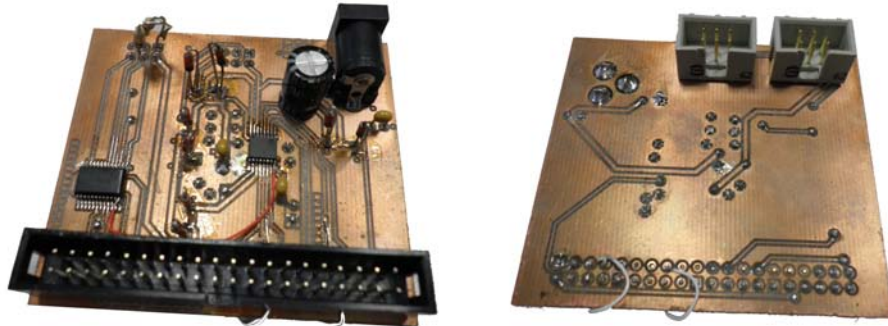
Placa auxiliar de motores. Vistas frontal y trasera.
